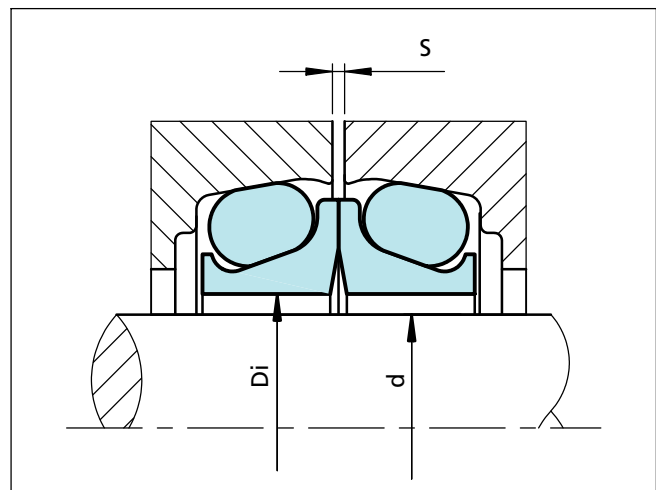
Wälzlagerstahlausführung mit glatter und zylindrischer Bearbeitung am Innendurchmesser
